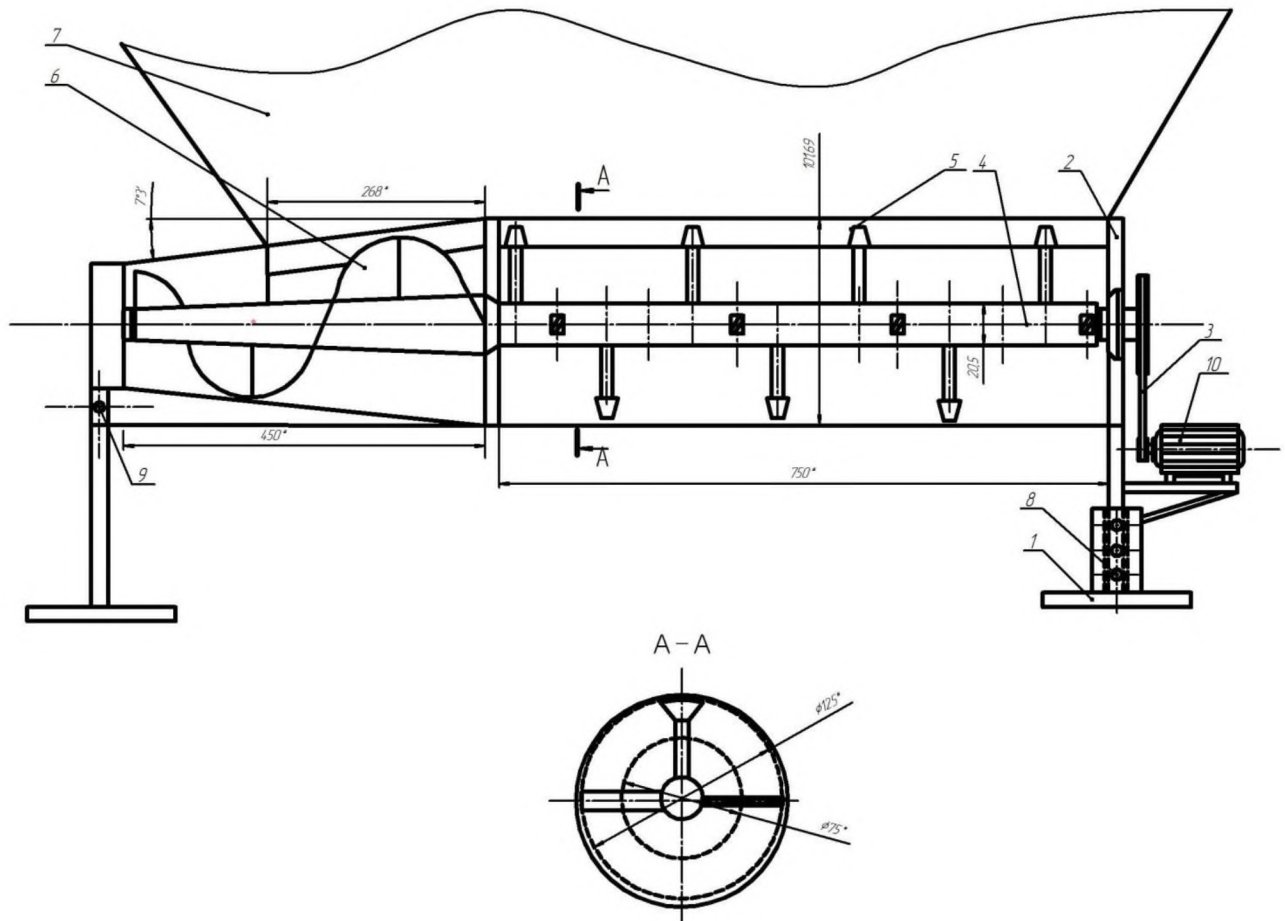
Схема дослідної установки для визначення параметрів пристрою подачі добрив на поверхню поля: 1- стаяк; 2- корпус; 3- пасова передача; 4- вал; 5- рихляча частина; 6- гвинтова частина; 7- бункер; 8- фіксатор; 9- шарнір; 10- електричний привід
